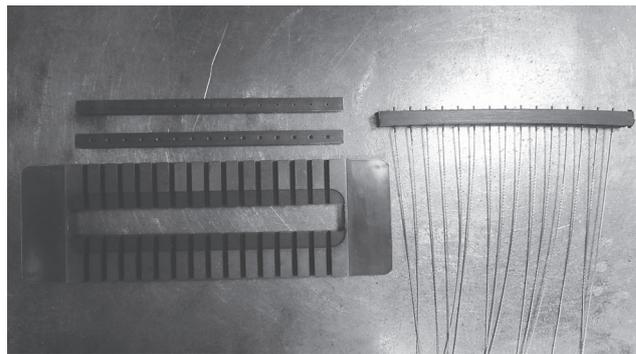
Пресс-форма, пластины с проходными отверстиями и готовый резинокордный блок метода потребителя № 1
